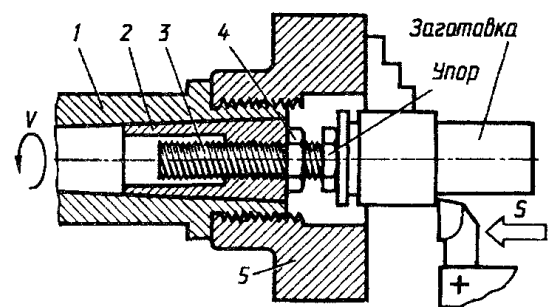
Шпindelний упор: 1 - шпindel; 2 - конусна втулка; 3 - гвинт упора; 4 - контргайка; 5 - патрон
